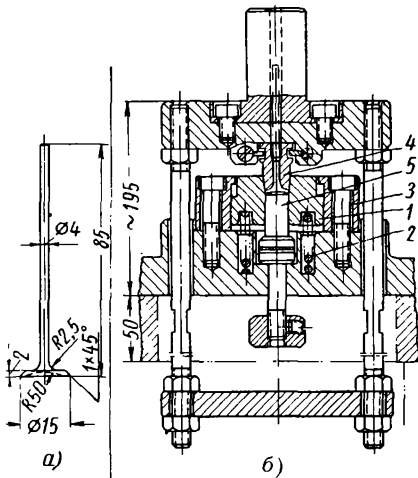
Штамп для изготовления поковки штока обратным выдавливанием в один переход: а — поковка; б — штамп
